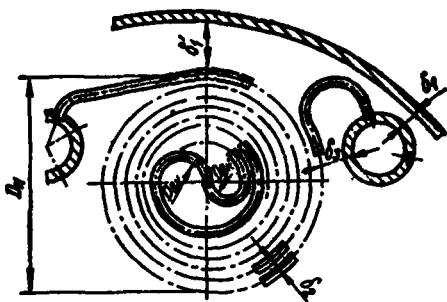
Схема расположения однолобостной спиральной трубы в корпусе коллекторного подогревателя высокого давления
